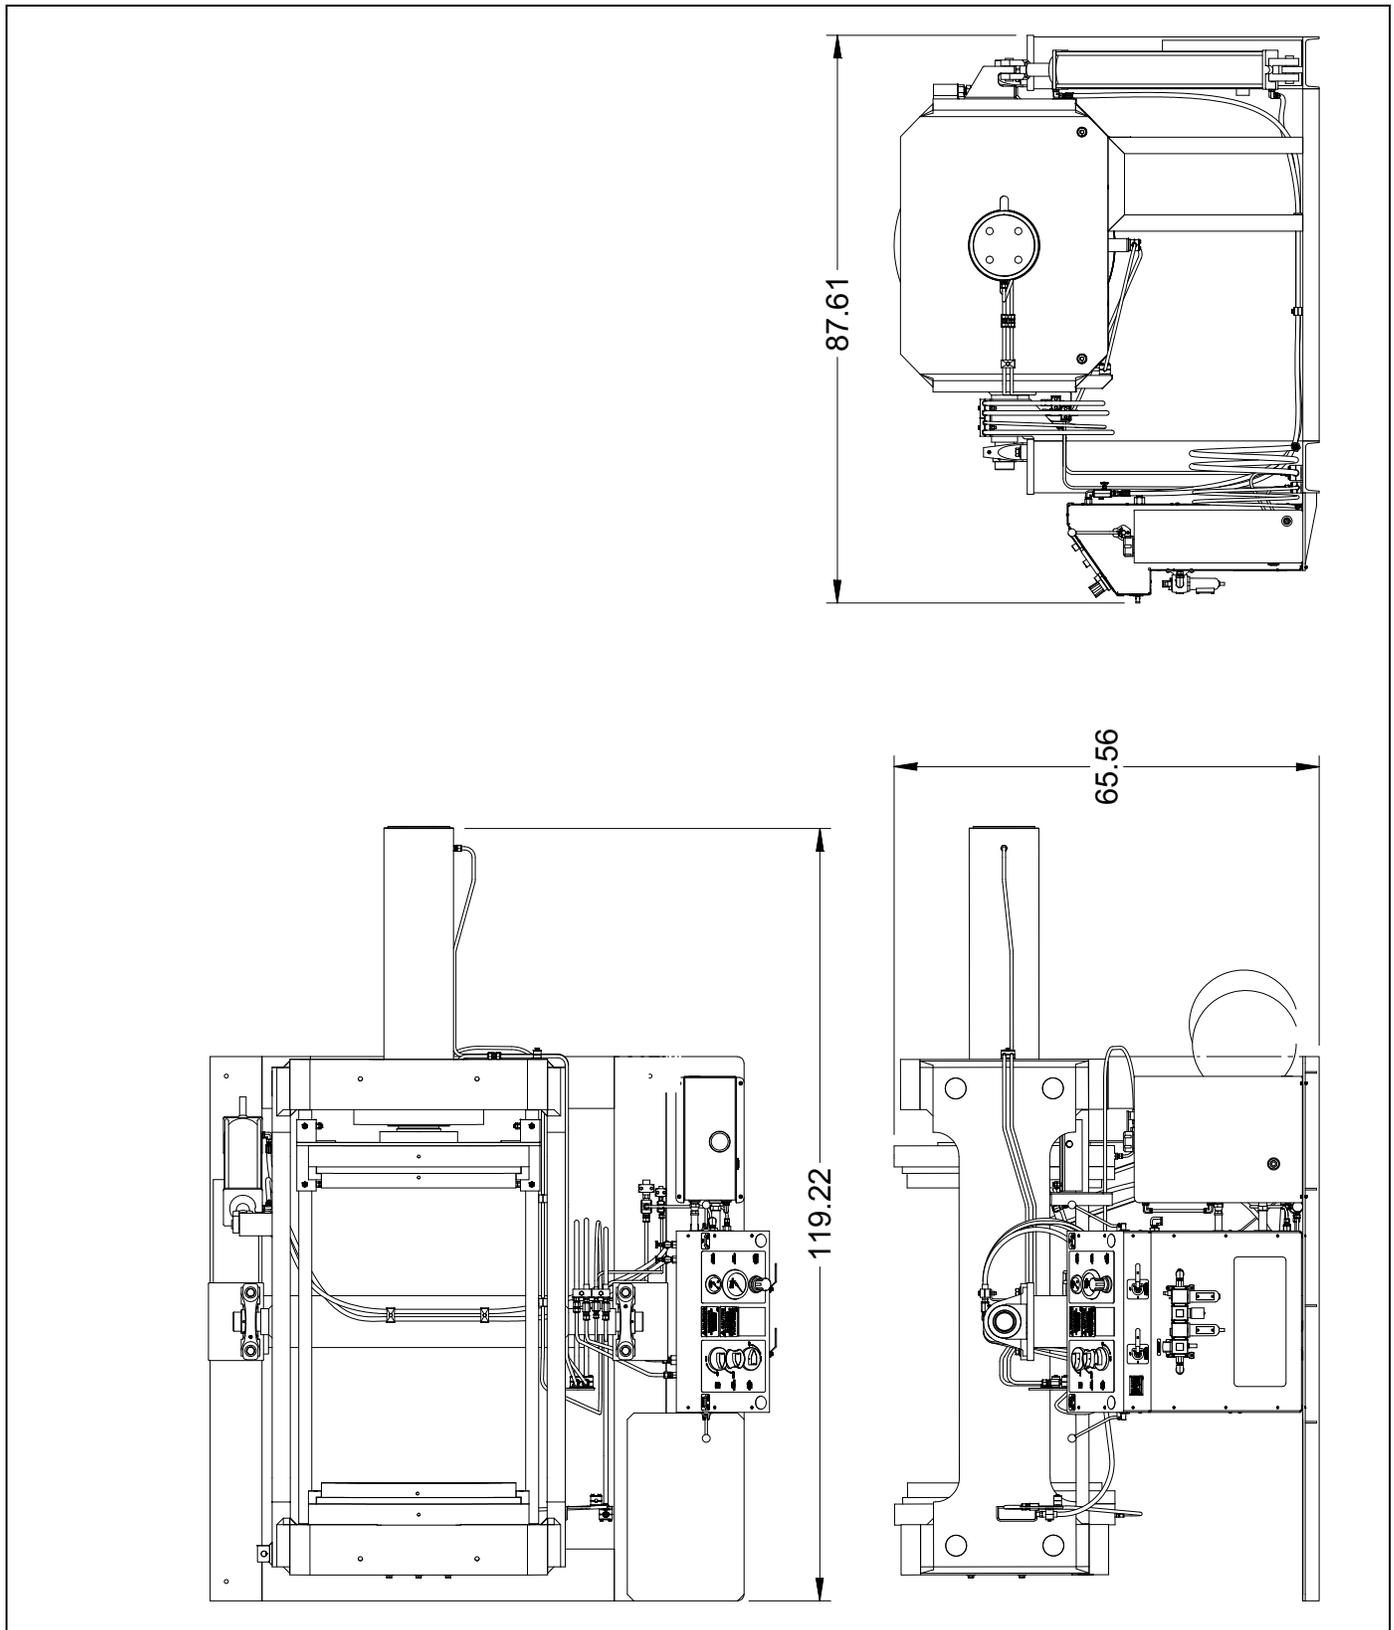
DIMENSIONS DU SYSTÈME DE SERRAGE
